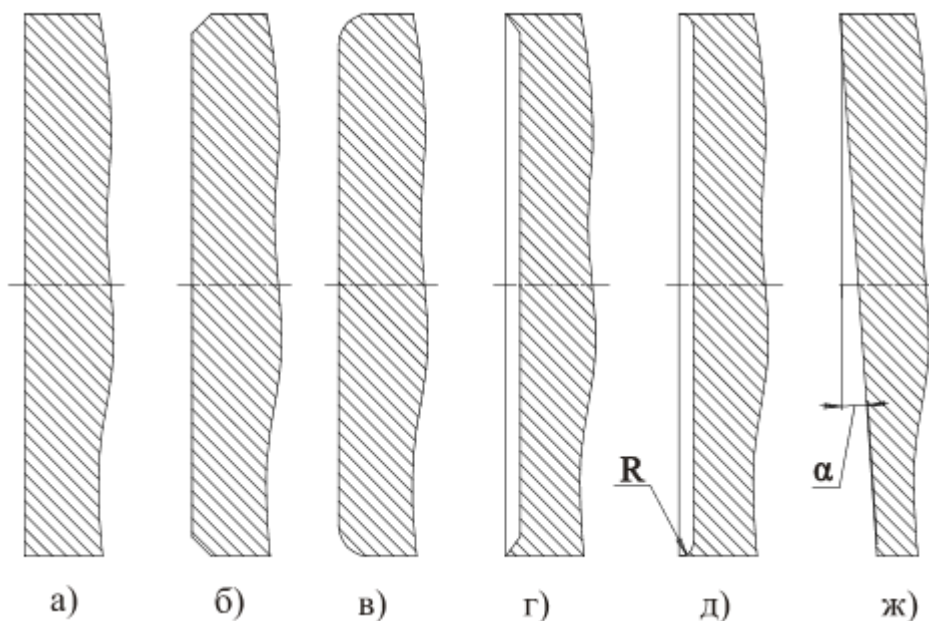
Конструктивні виконання контактуючих поверхонь поршнів дозатора: а - базова конструкція; б - з зовнішніми фасками; в - з зовнішніми заокругленнями; г - з внутрішніми фасками; д - з внутрішніми заокругленнями; ж - з похилою поверхнею.
